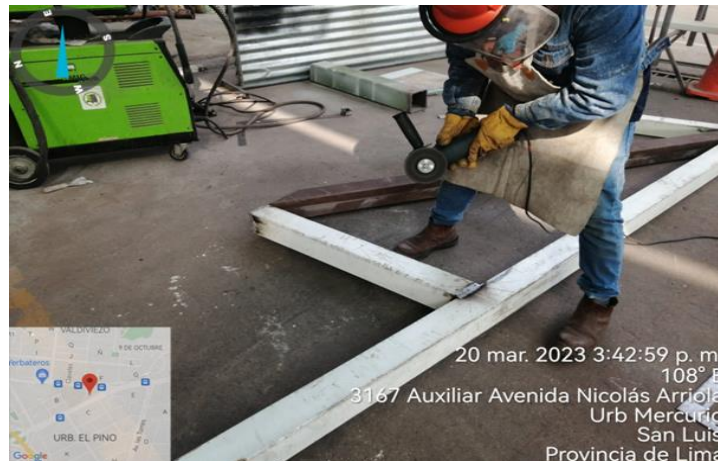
Esmerilado. Fuente: Elaboración Propia.
